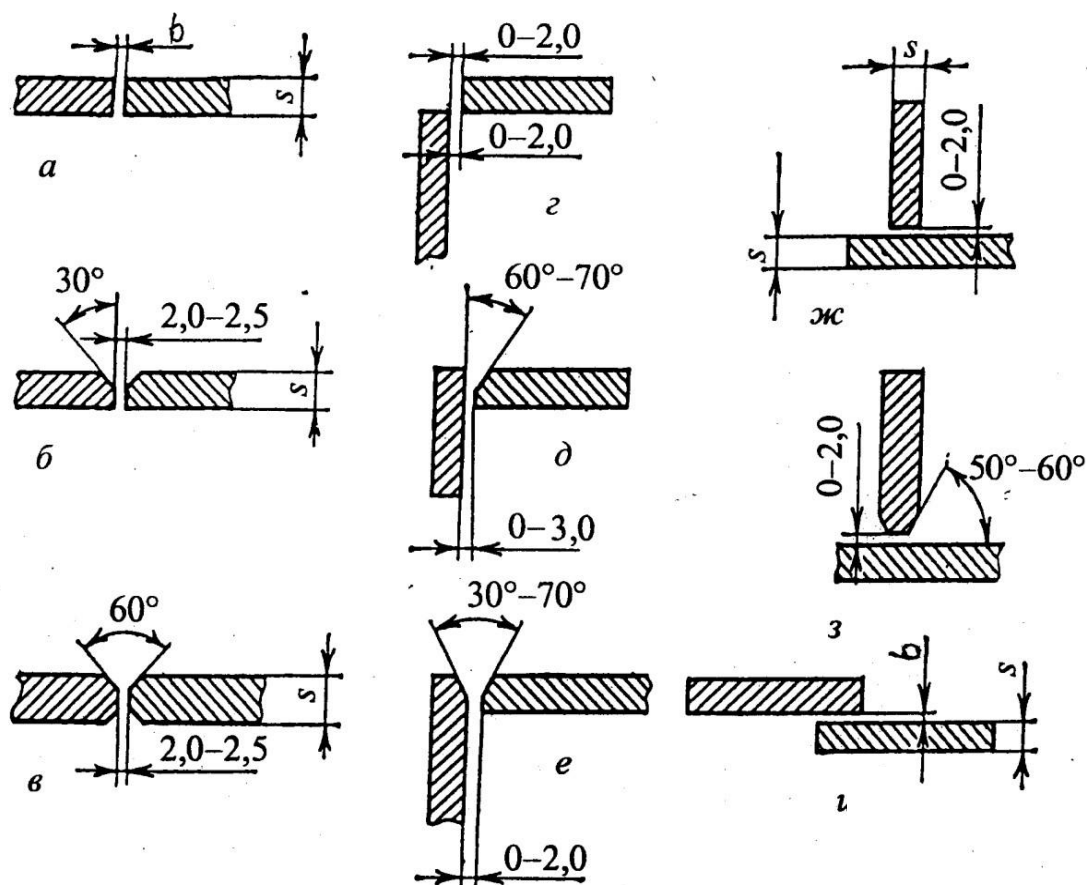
Типи зварних з'єднань під час ручного дугового зварювання
